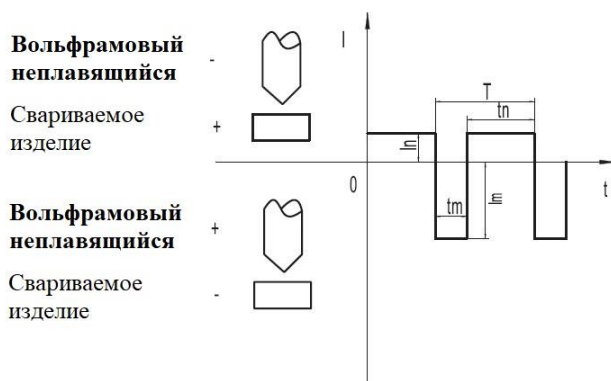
Форма волны и параметры при сварке переменным током
